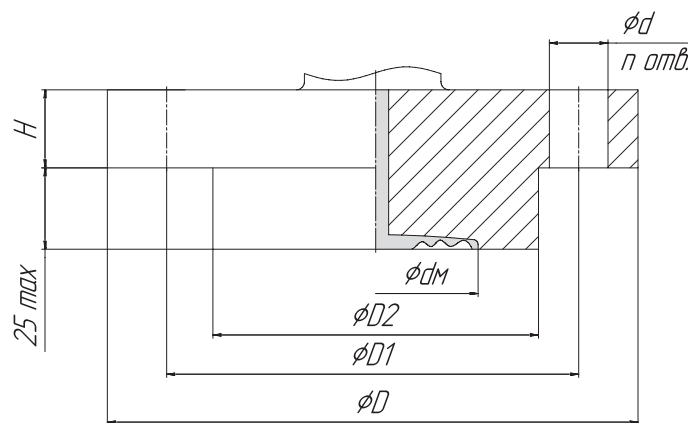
Габаритные и присоединительные размеры фланцев с плоской мембраной по DIN EN 1092-1, ASME
